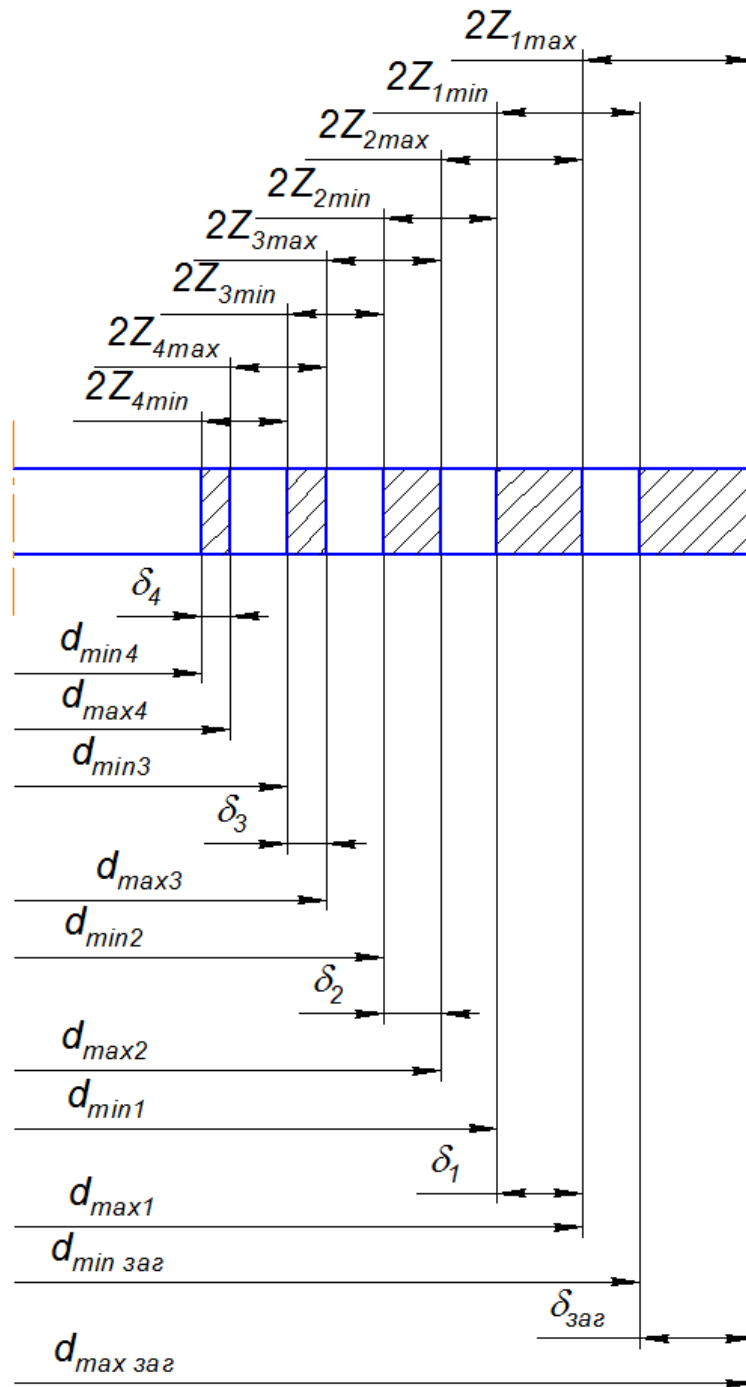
Схема розташування припусків по технологічним операціям обробки деталі класу “вали”
